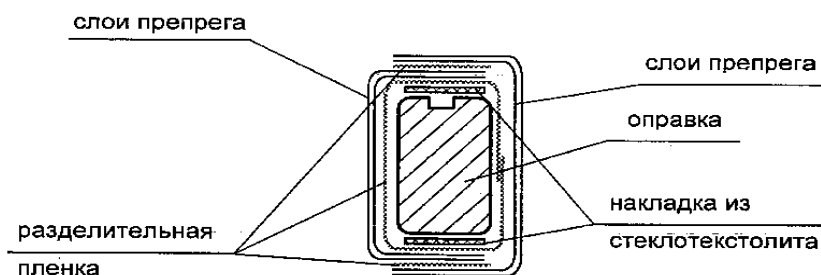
Схема выкладки заготовок пояса двустенных нервюр для подформовки
